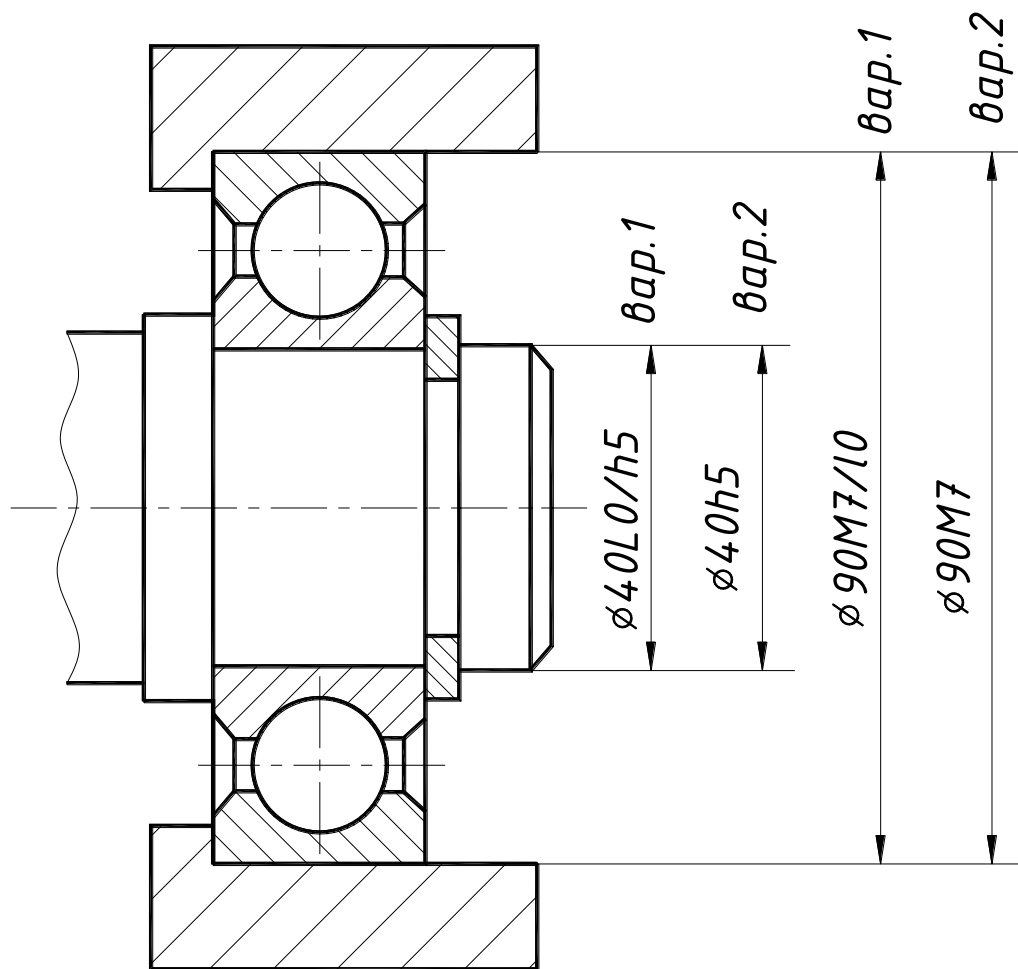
Ескіз робочого креслення з'єднання підшипника з валом і отвором корпусу
